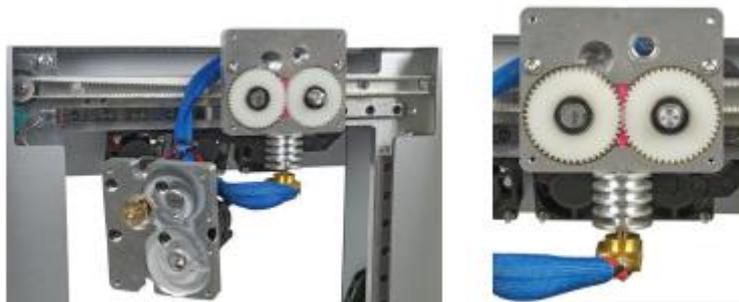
Печатающая головка и регулировка прижима нити PLA
